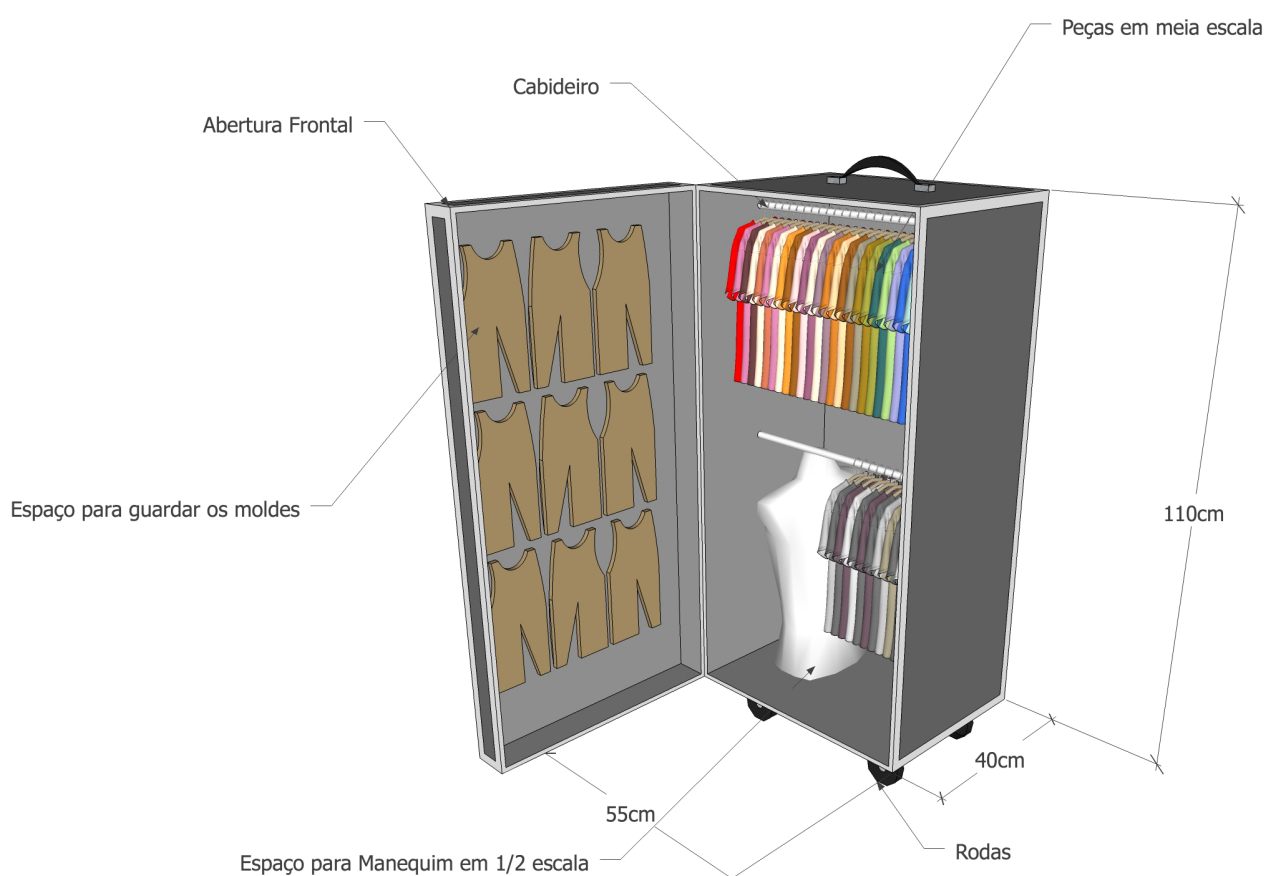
Desenho esquemático do produto técnico. Fonte: autora.
